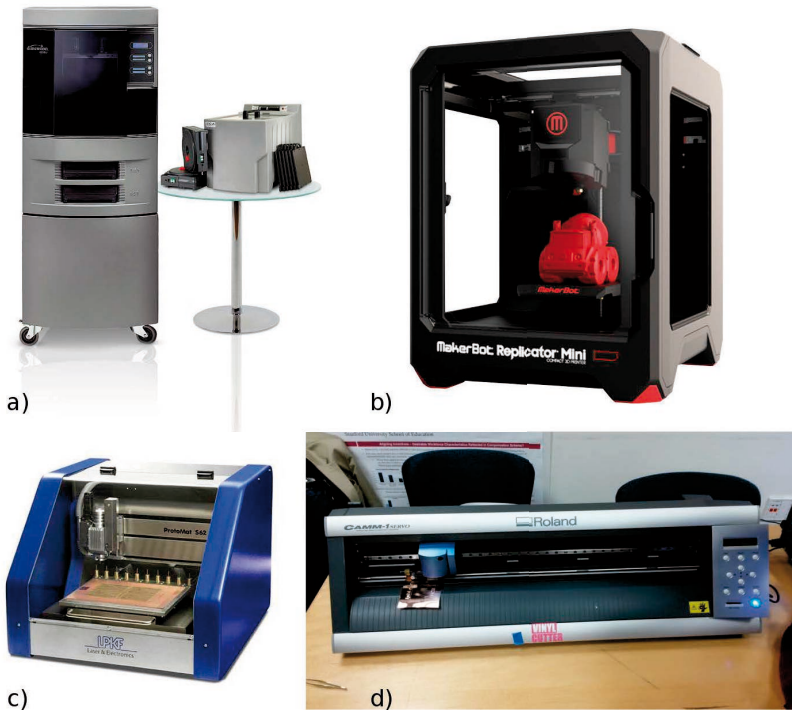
Die professionellen, teuren Maschinen der Industrie und ihre preisgünstigen Pendants für Hobbyisten. a) Dimension Elite 3D-Drucker, ca. 30.000 CHF, b) Makerbot Replication Mini ca. 1.000 CHF, c) LPKF Circuit Printer ca. 15.000 CHF, d) Camm 1-servo vinyl cutter ca. 1.000 CHF.
